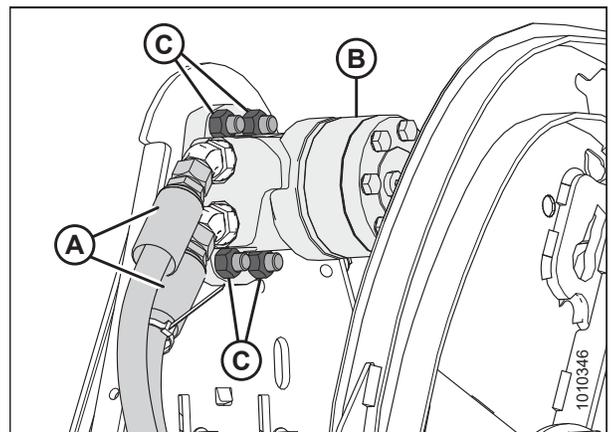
Haspelmotor und Hydraulikschläuche
